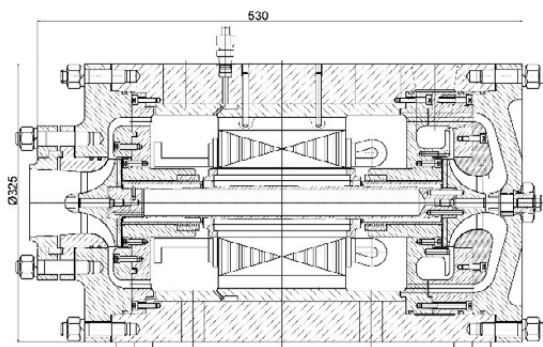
Опытный образец компрессора АО «Вниихолодмаш»
